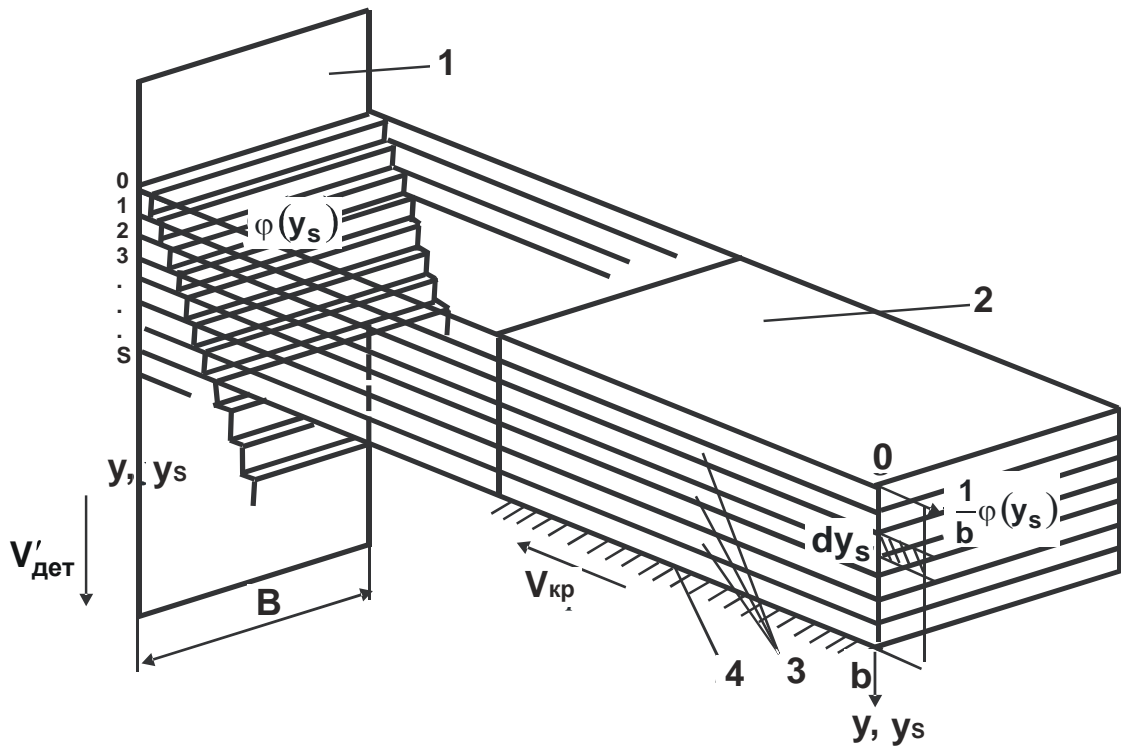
Розрахункова схема закону розподілу вершин проєкцій зерен на рухомій площині: 1 – рухома площина; 2 – елементарний об'єм робочої поверхні круга; 3 – зерна круга; 4 – рівень зв'язки круга
